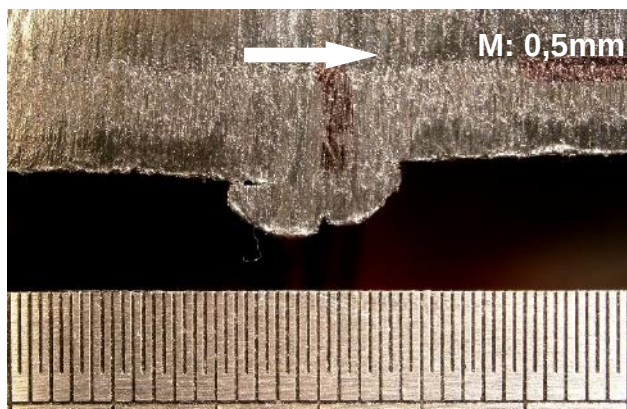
Detail ustavení aparátu vůči vzorku
